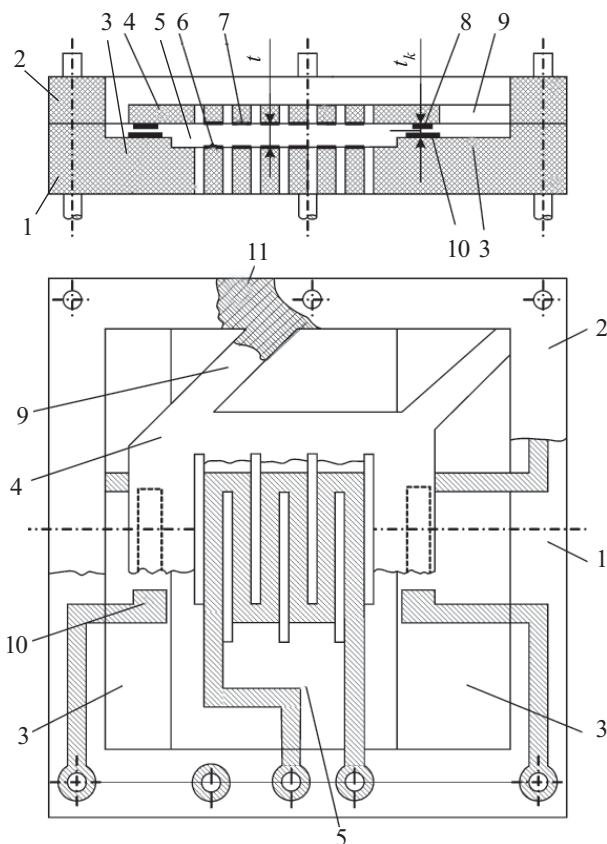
Конструктивная схема электротокового микрореле: 1 — подложка; 2 — диэлектрическая пластина; 3 — ступеньки в подложке; 4 — подвижный якорь; 5 — углубление в подложке; 6 — неподвижный МУ; 7 — подвижный МУ; 8 — перемычки; 9 — упругие держатели; 10 — контакты; 11 — рамка пластины
